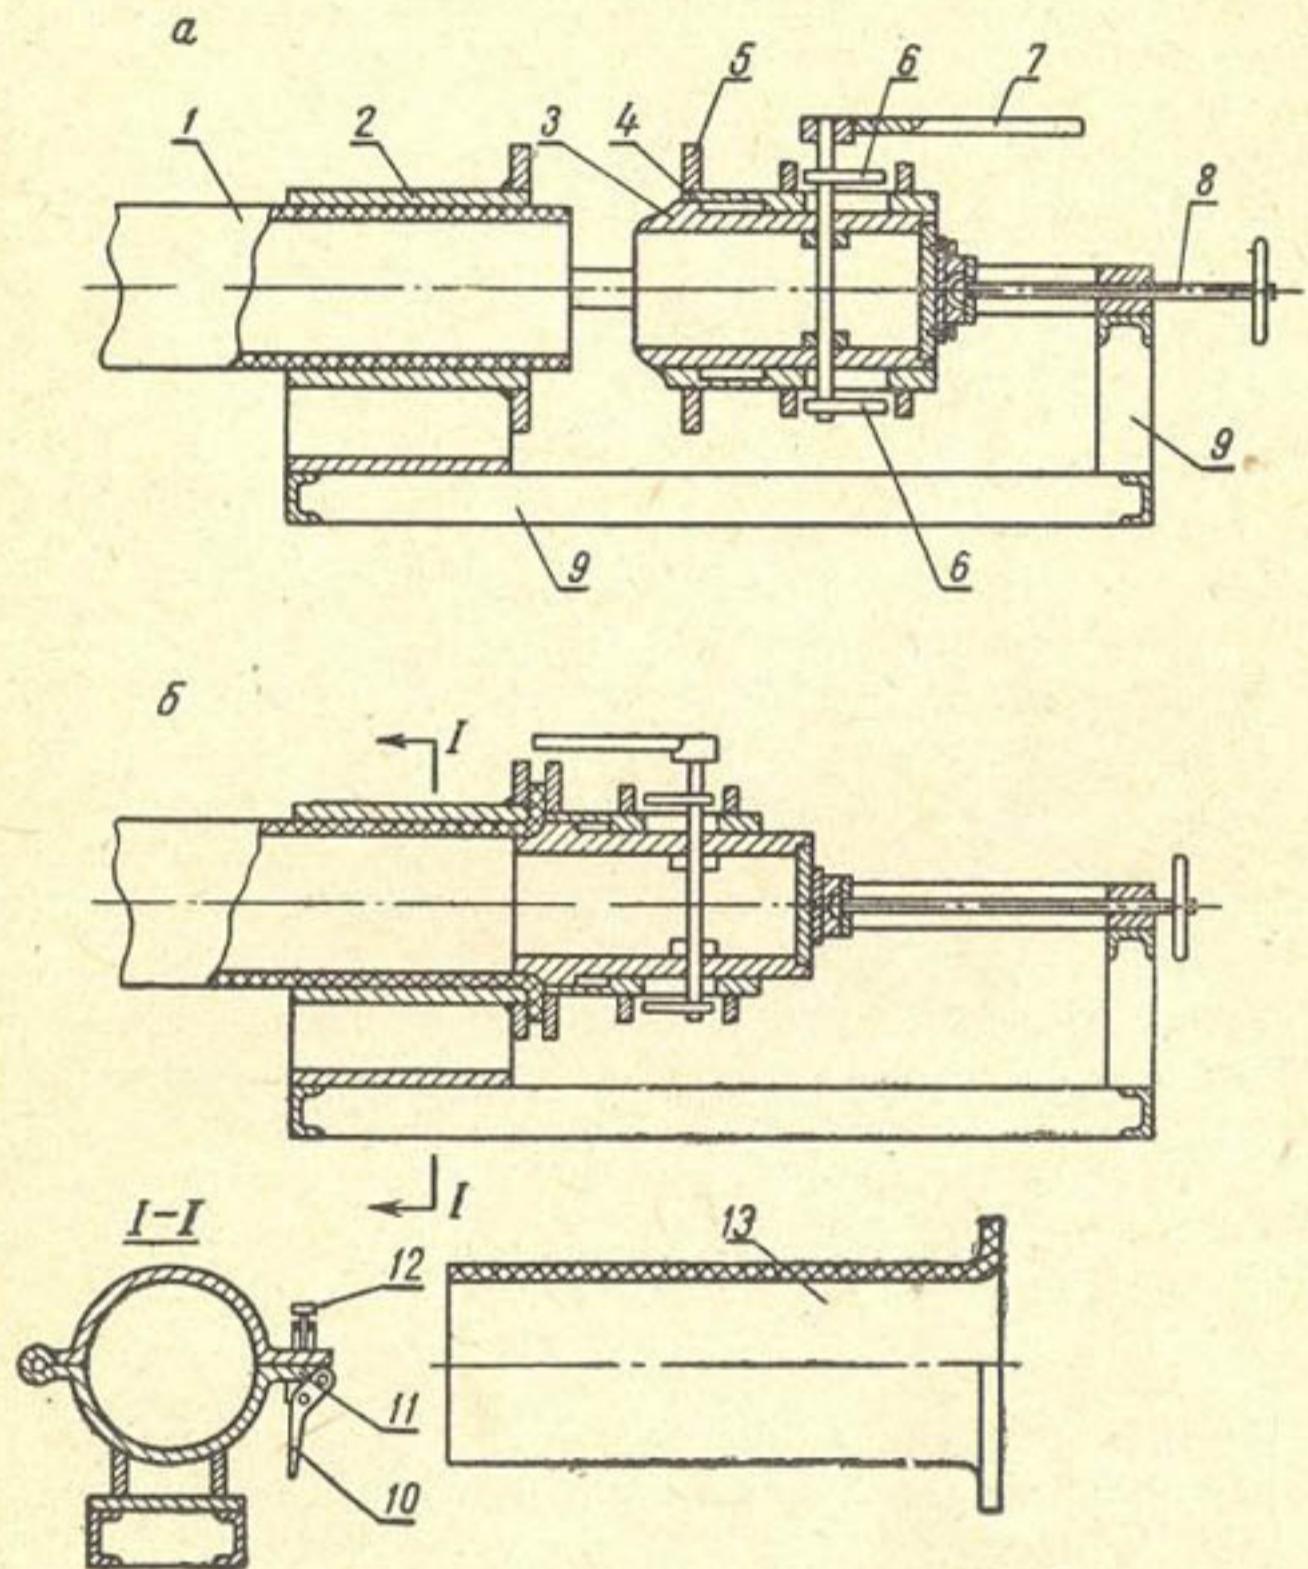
Схема установки для формовки буртика на пластмассовых трубах:
